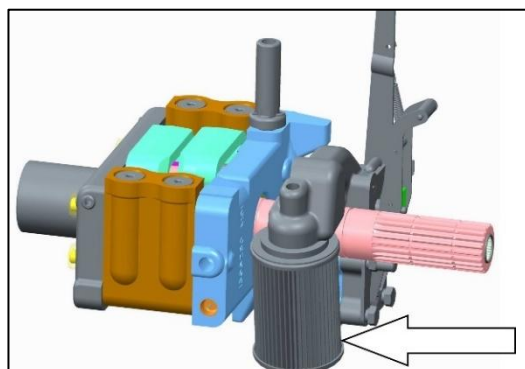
FILTRE D'ASPIRATION DE LA POMPE HYDRAULIQUE
